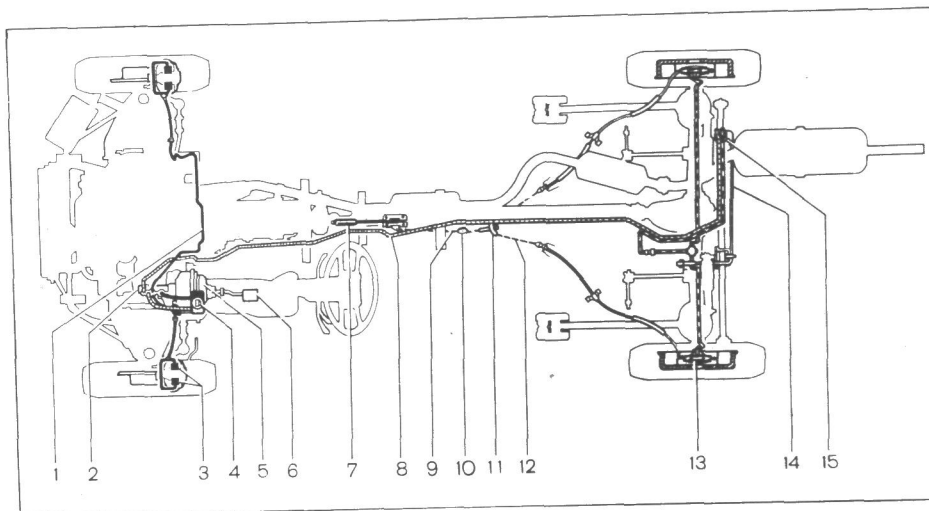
Схема тормозной системы: 1 — контур передних тормозов; 2 — главный цилиндр гидропривода тормозов; 3 — тормозные цилиндры переднего дискового тормоза; 4 — бачок гидропривода тормозов; 5 — вакуумный усилитель; 6 — педаль тормоза; 7 — рычаг стояночного тормоза; 8 — контур задних тормозов; 9 — передний трос стояночного тормоза; 10 — направляющий ролик переднего троса; 11 — уравниватель заднего троса; 12 — задний трос стояночного тормоза; 13 — колесный цилиндр заднего барабанного тормоза; 14 — торсионный рычаг регулятора давления; 15 — регулятор давления
